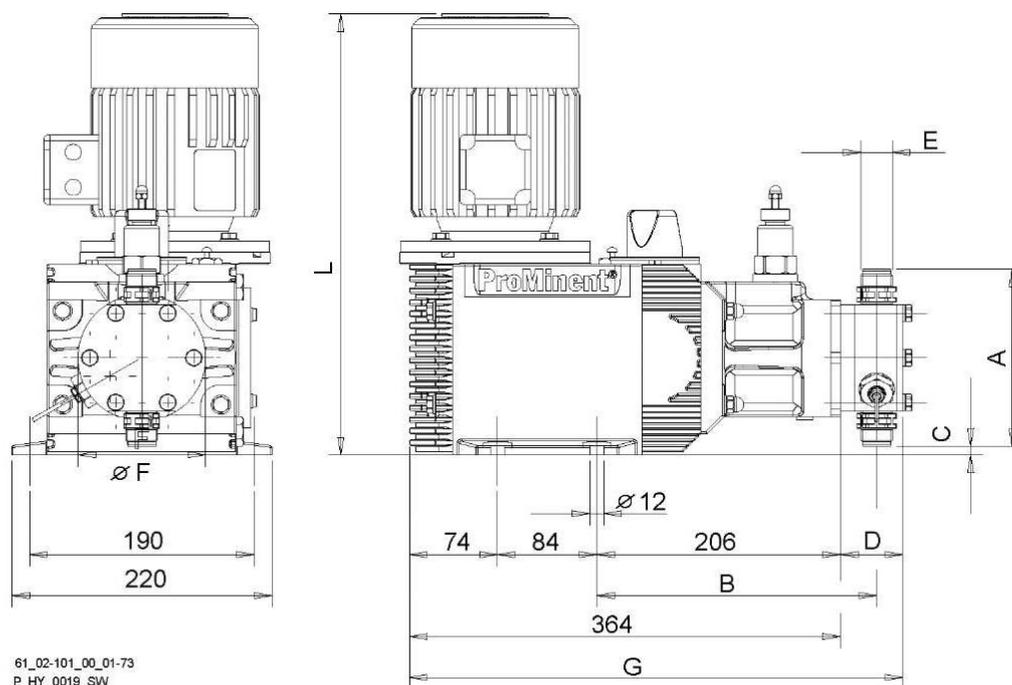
Габаритный чертеж Hydro HP2 (HP2a H). Размеры в мм.
